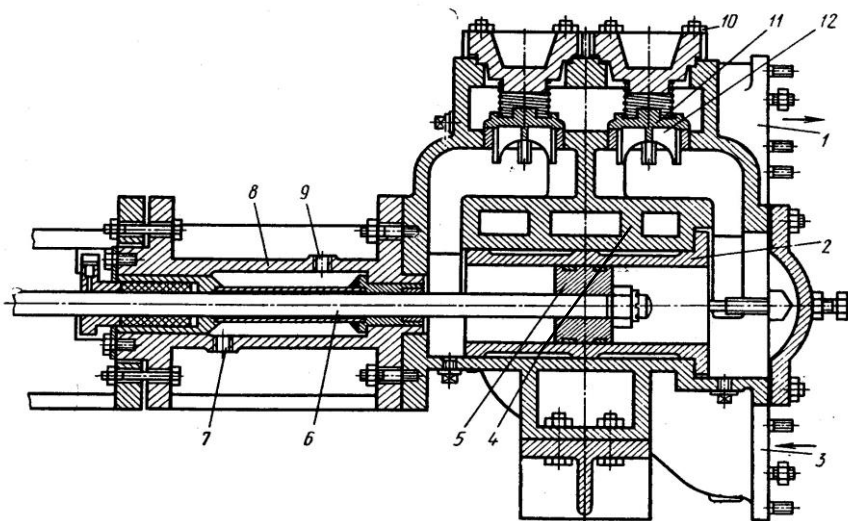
Гидравлическая часть двухцилиндрового парового прямодействующего насоса: 1 – напорный патрубок; 2 – цилиндрическая втулка; 3 – всасывающий патрубок; 4 – клапанная коробка (цилиндр); 5 – поршень; 6 – поршневой шток; 7 и 9 – отверстия соответственно для входа и выхода охлаждающей воды; 8 – сальник, охлаждаемый водой; 10 – клапанная крышка; 11 – пружина клапана; 12 – тарельчатый клапан.
